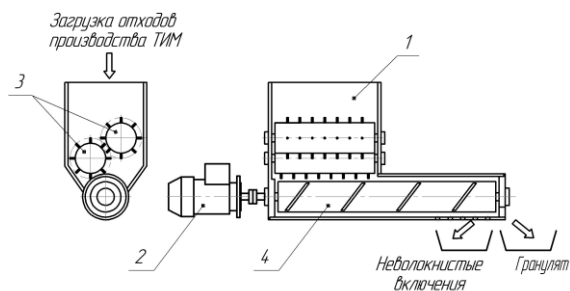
Схема установки получения сыпучего волокнистого материала из минеральной ваты: 1 – бункер загрузочный; 2 – привод; 3 – валы измельчающие; 4 – шнек транспортирующий
